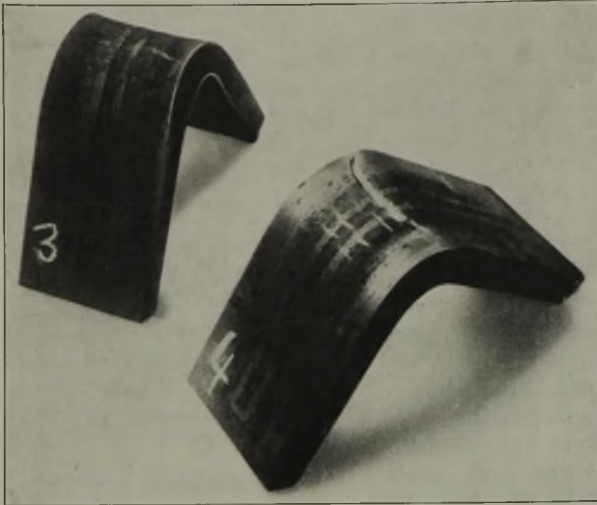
Biegeproben, bei denen ein Steg zunächst mit Kehlnähten aufgeschweißt und dann einschließlich der Kehlnähte wieder abgehobelt wurde.
